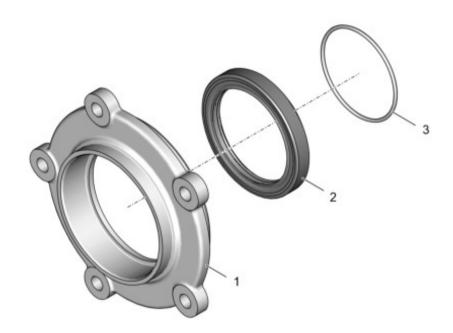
375-1802026-02 Крышка передняя подшипника первичного вала с манжетами
